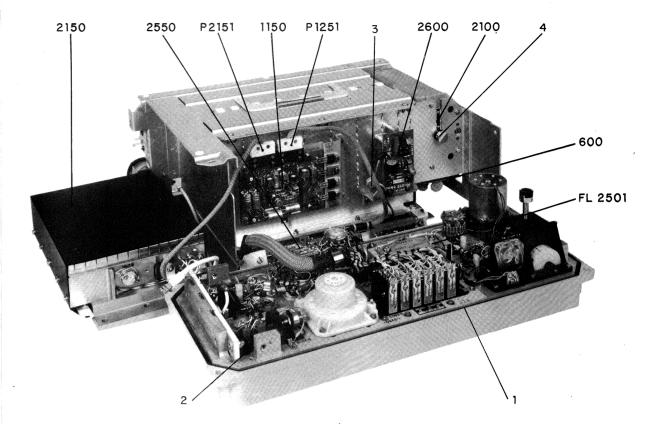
Vue d'ensemble Fig.3 Comprehensive view
